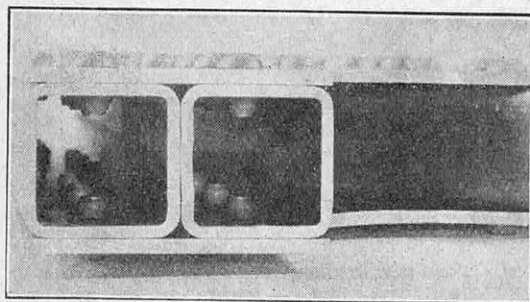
ET 4. — CES EXEMPLES D'ASSEMBLAGES MONTRENT QUE LE NOUVEAU PROCÉDÉ DE RIVETAGE A L'EXPLOSIF S'APPLIQUE AU CAS OU LA DEUXIÈME TÊTE DU RIVET EST PEU ACCESSIBLE
